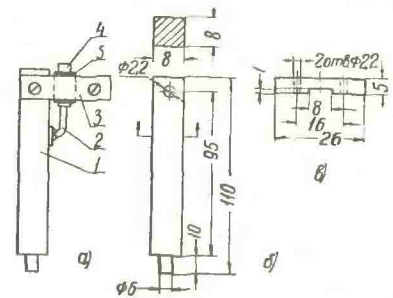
Узел крепления пьезокристалла ПЗК-3: а — сборочный чертеж: 1 — стойка, 2 — выводы кристалла, 3 — держатели кристалла, 4 — пьезокристалл, 5 — прокладка из губчатой резины; б — стойка (деталь 1). Материал — дерево; в — держатели кристалла 2 шт. (деталь 3). Материал — текстолит или органическое стекло.
